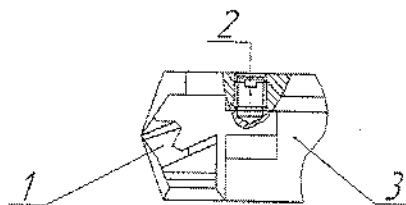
Крепление твердосплавной головки к корпусу инструмента: 1 – сменная твердосплавная головка ISCAR IDI 080 SG;
